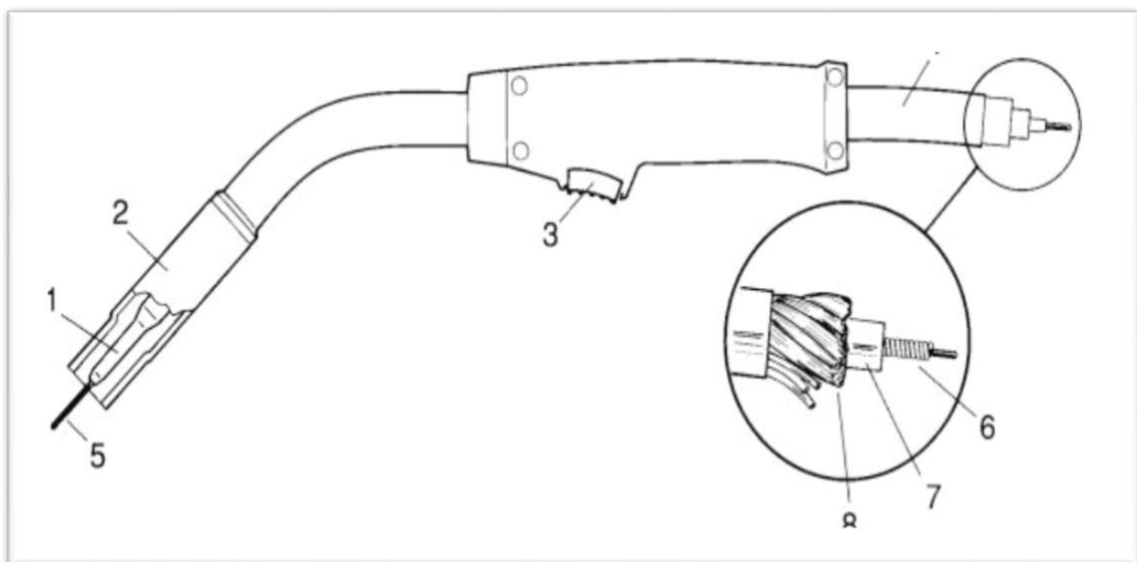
Pistolet de soudage avec flexible. [6]
